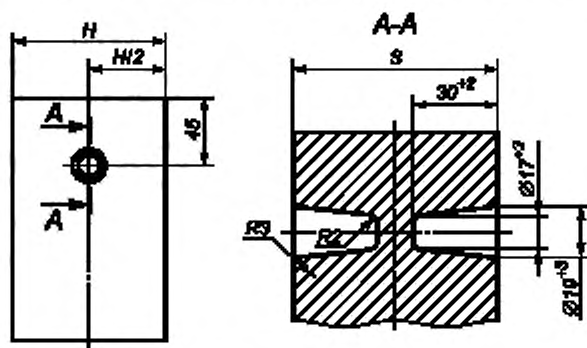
Размеры отверстий для штырей. Вариант 2
